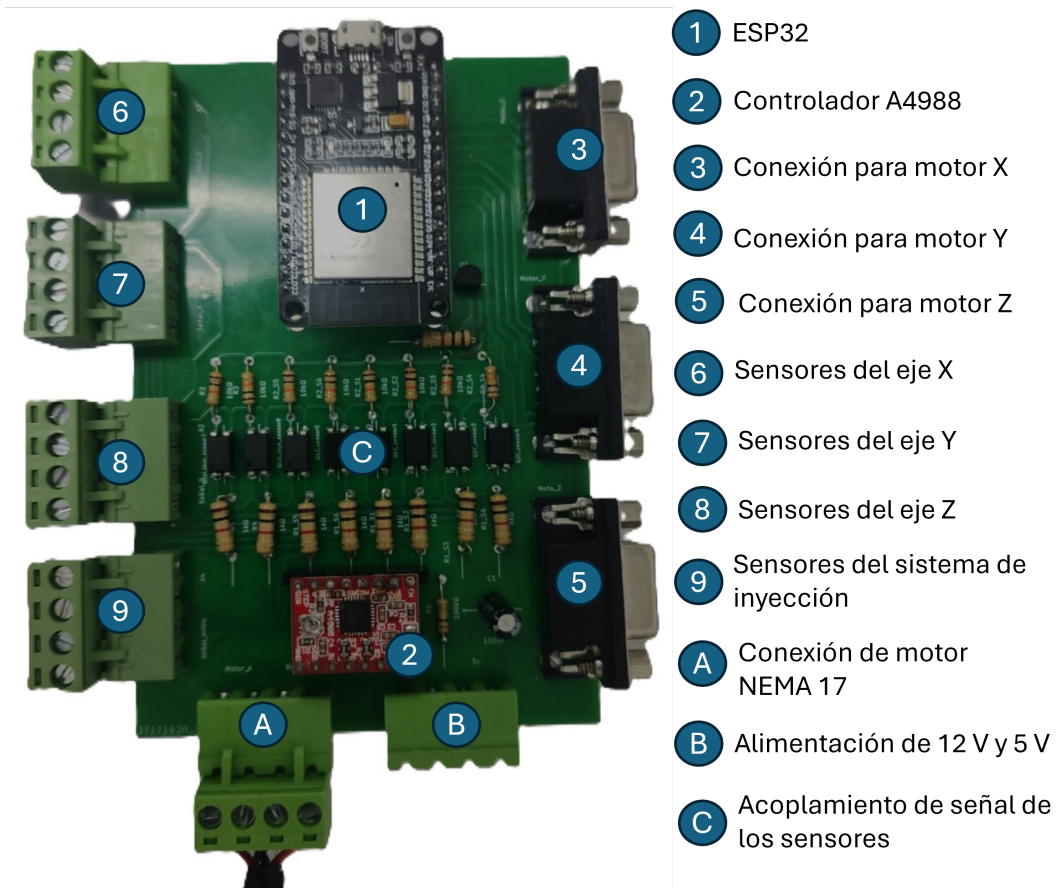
PCB con los componentes electrónicos soldados.
